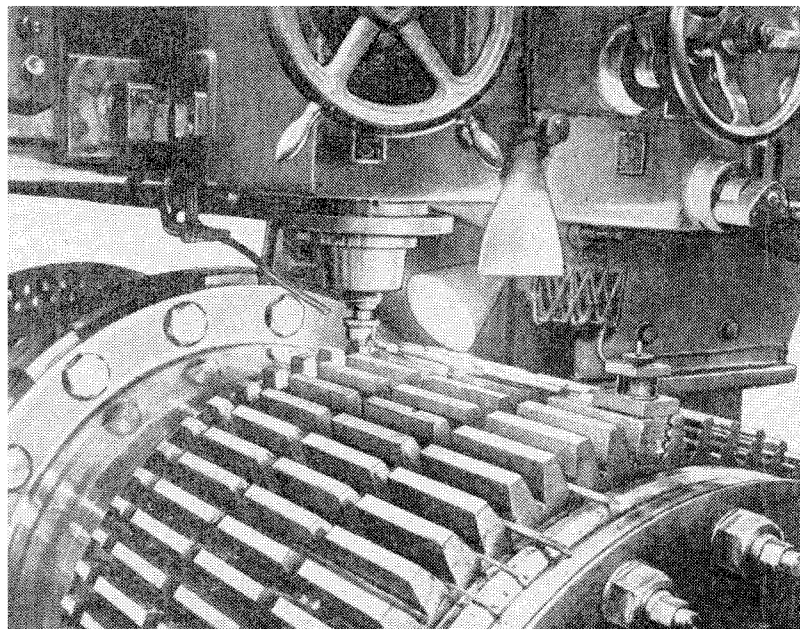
Схема фрезерования пазов под лопатки в роторе газовой турбины
